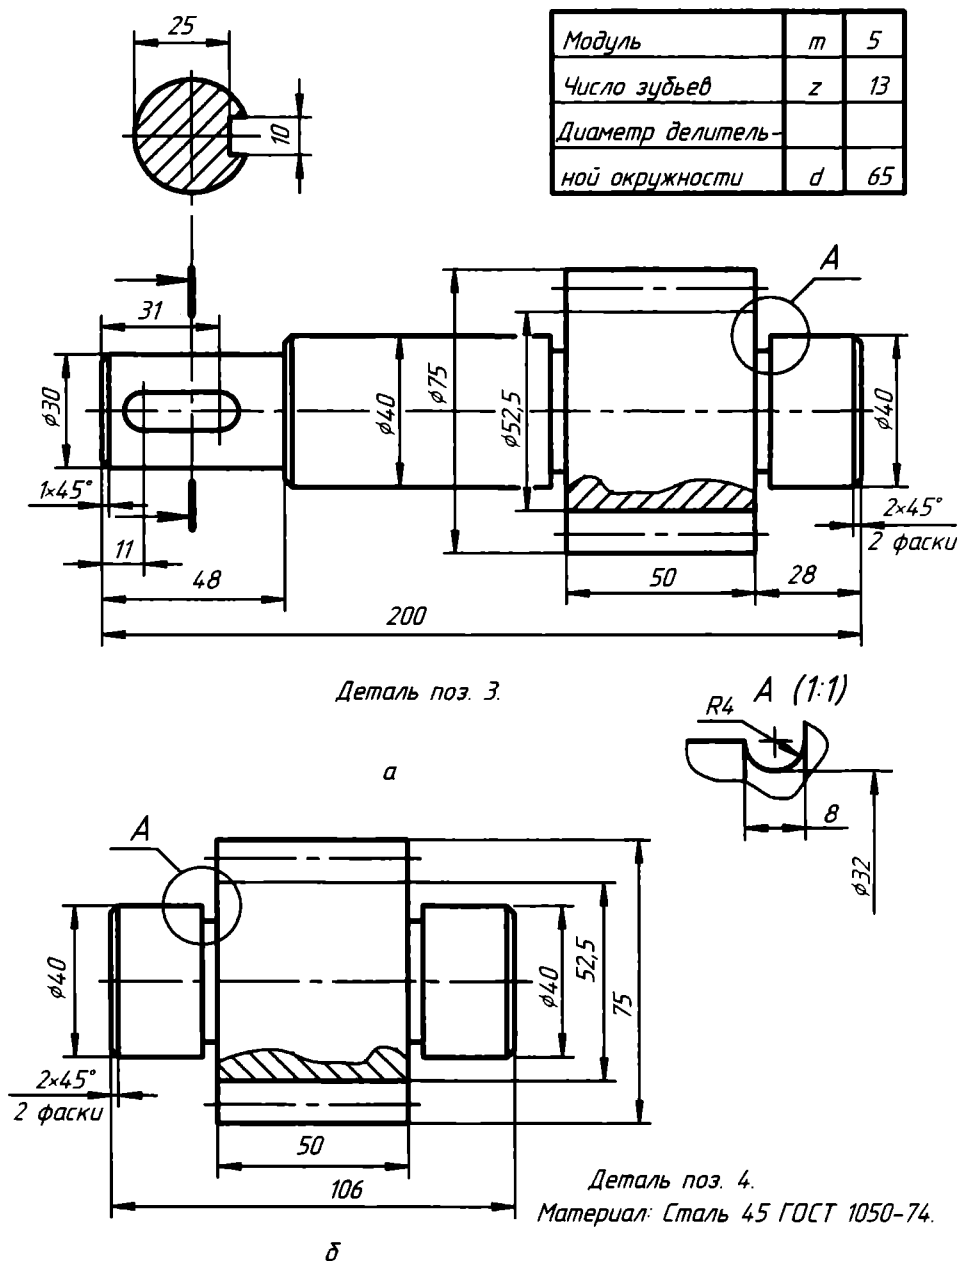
Чертежи зубчатых колес: а — ведущего; б — ведомого
